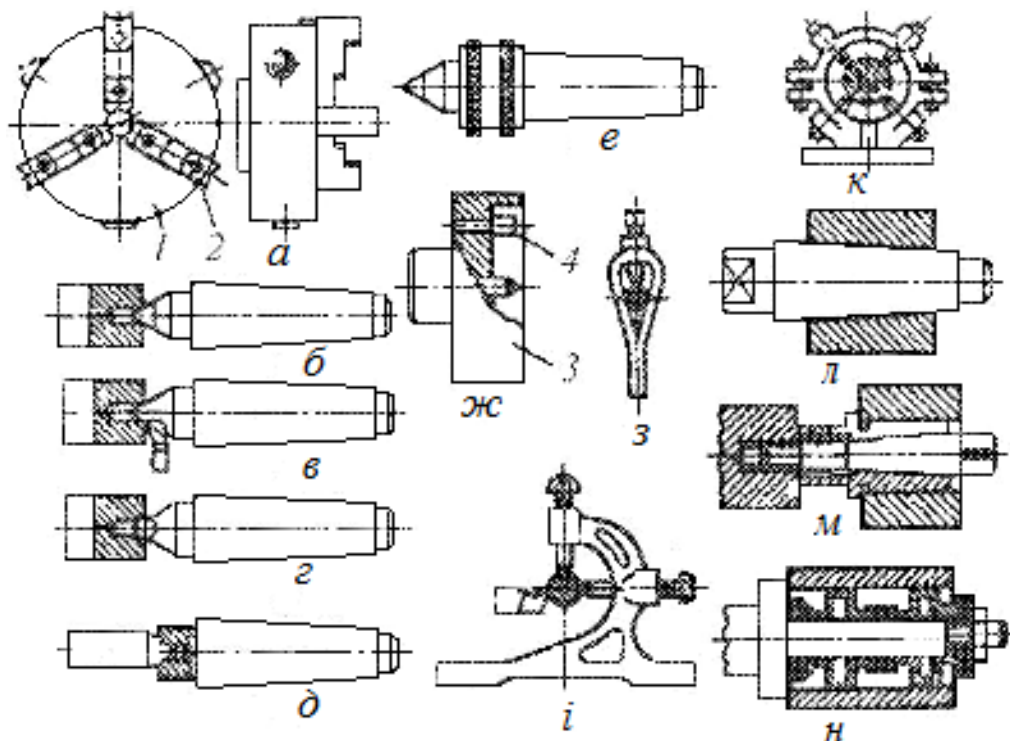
Пристрої для закріплення заготовок на токарних верстатах
